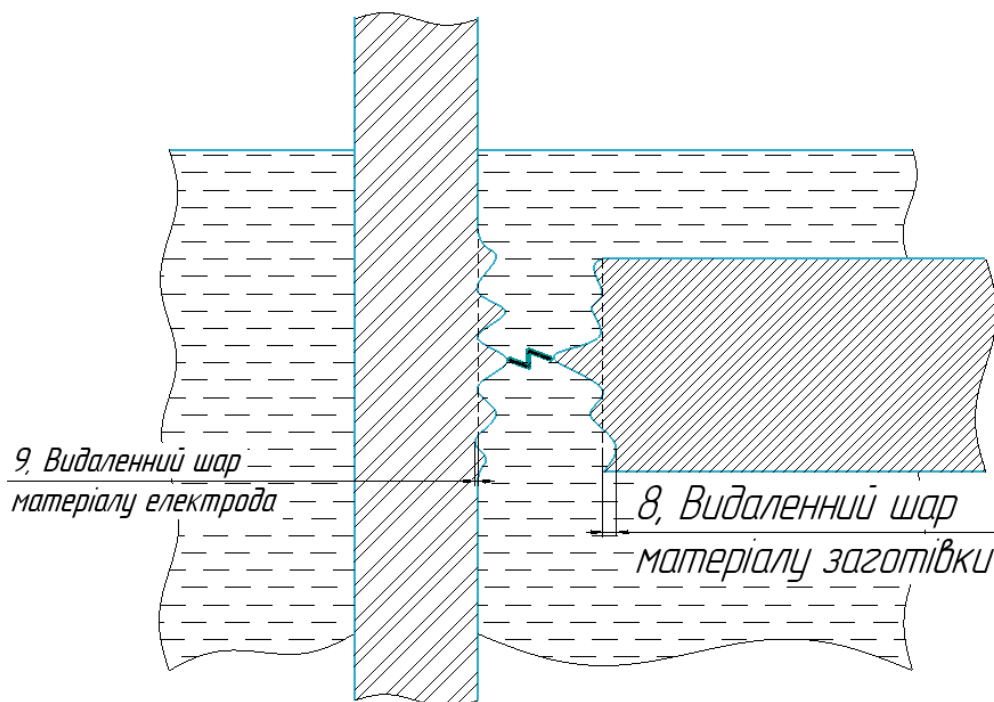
Видалений шар матеріалу заготовки і електрода [6, с.62-89]
